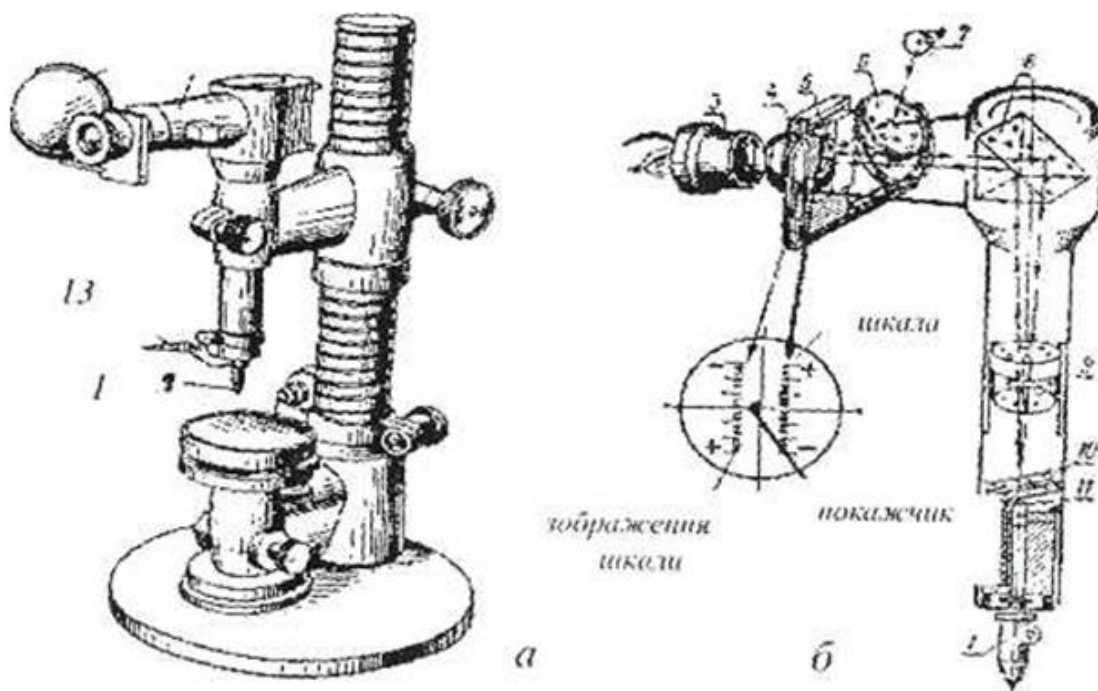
Вертикальний оптиметр (а) і його схема (б): 1 - вимірювальний стержень; 2 - пружина; 3 - окуляр; 4 - скляна пластинка з шкалою;
